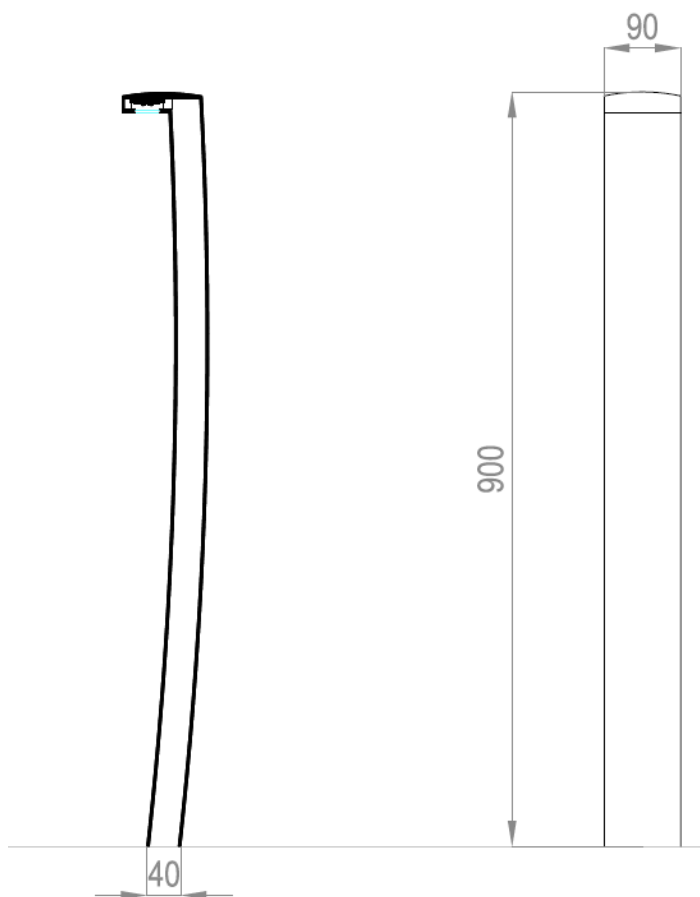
Vista in sezione longitudinale e in prospettiva della soluzione bollard
